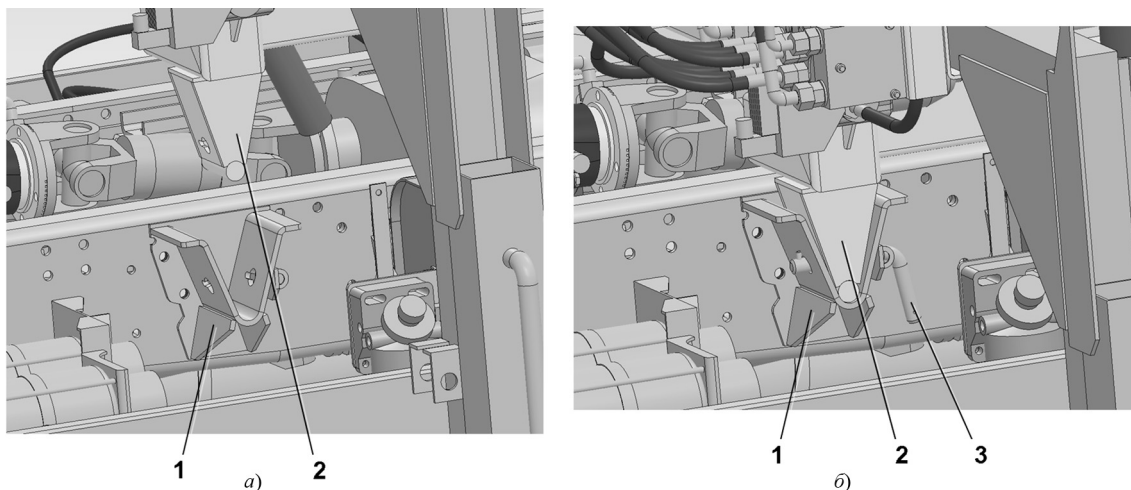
Универсальный механизм установки до сборки (а) и в сборе (б):
